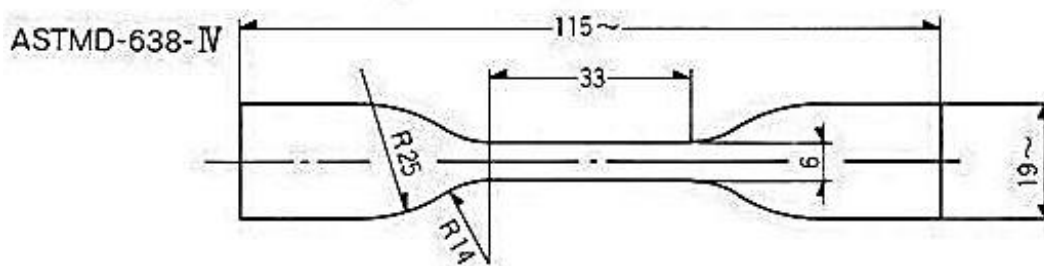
a: Dimensions des éprouvettes haltères de traction selon la norme ASTM D638 type 4 [36]
